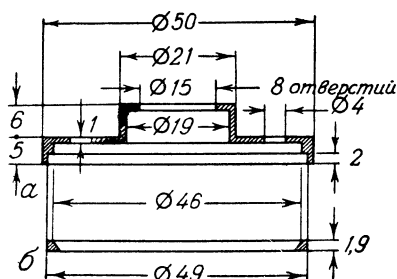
Размеры корпуса громкоговорителя а и прижимного кольца б
